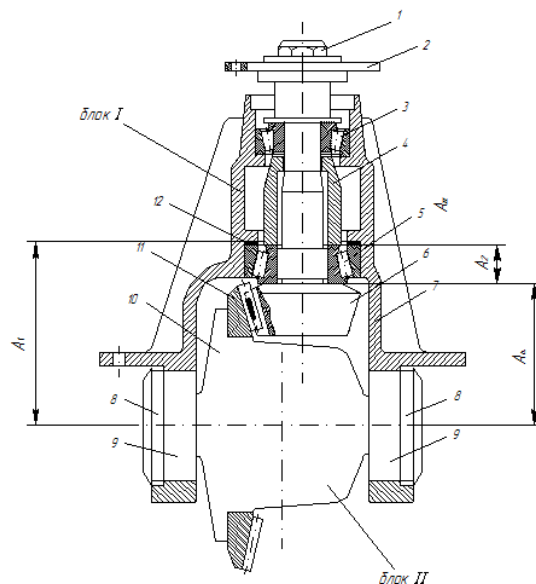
Конструктивная схема редукторов легкового автомобиля
